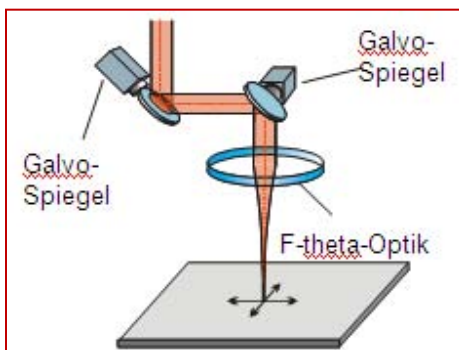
Prinzip des Quasisimultanschweißens
